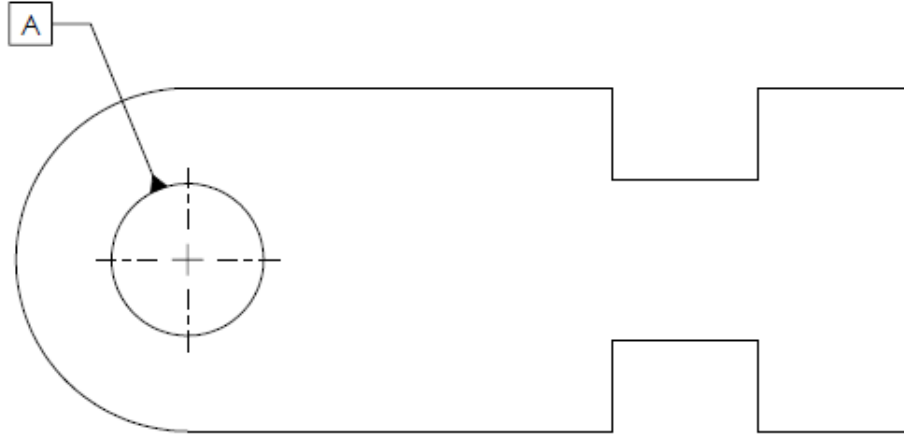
Şekil üzerinde datum gösterimi
